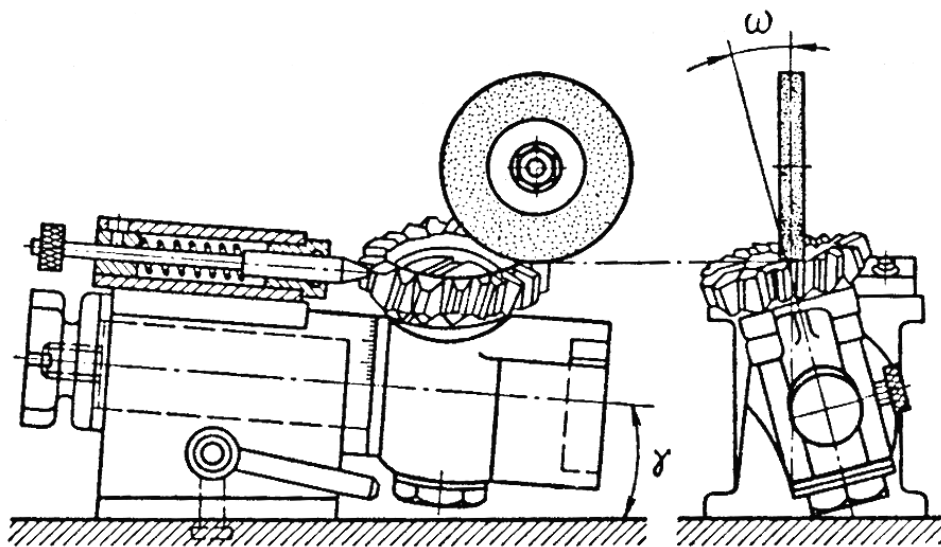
Приспособление для заточки косозубых долбяков на универсально-заточном станке
